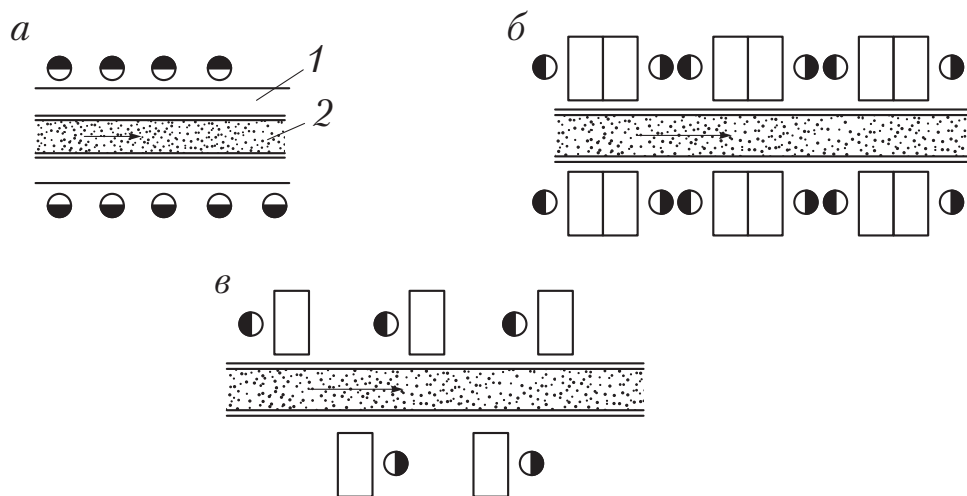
Схемы расположения сборочных мест при использовании ленточного конвейера:
